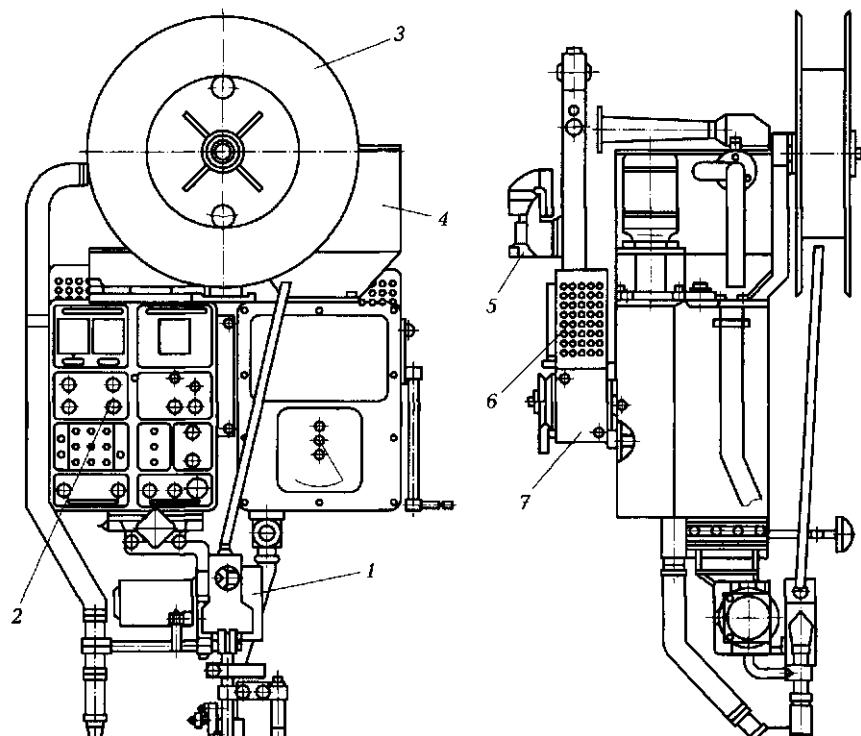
Сварочный автомат подвесного типа серии А-1400:
